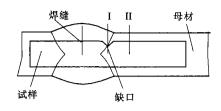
焊接接头冲击试验取样部位示意图 Fig. 2 Position of impact test samples from welded joint
